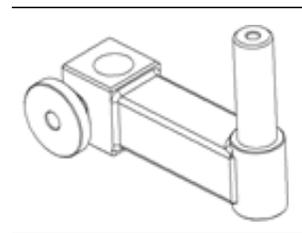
ПОВОРОТНЫЙ ПАТРОН
